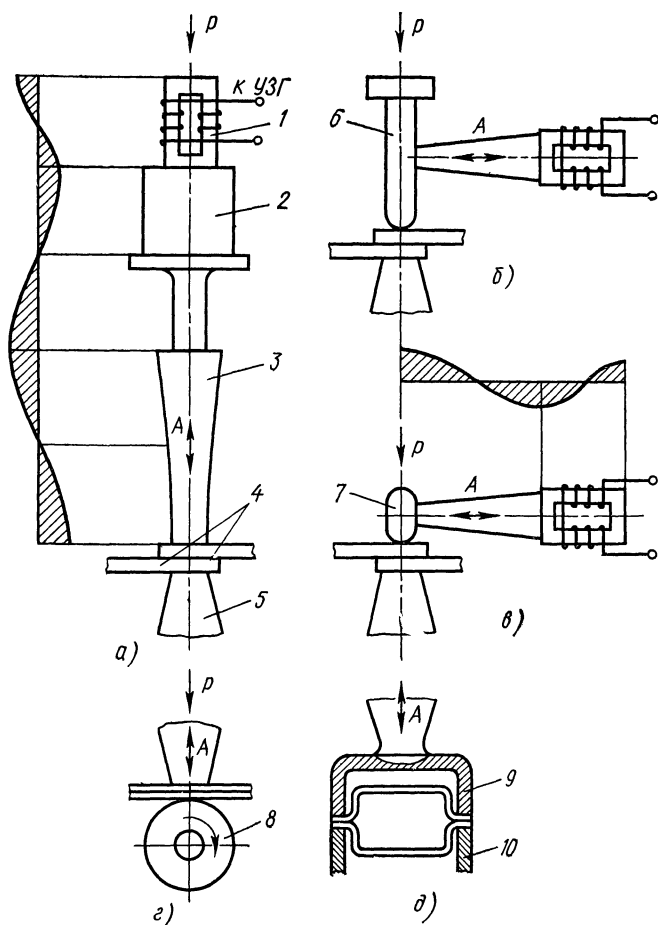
Кинематические схемы ультразвуковой сварки:
